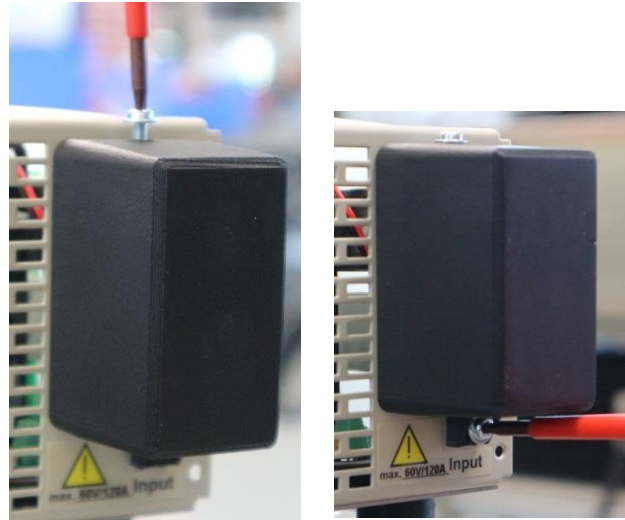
Anschrauben der Abdeckhaube für unbenutzte Lasteingänge
